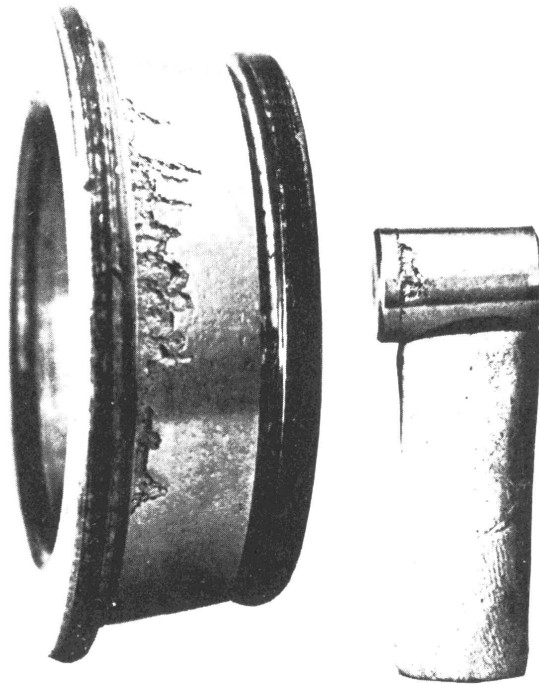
모서리 하중에 의해 발달된 Spalling
